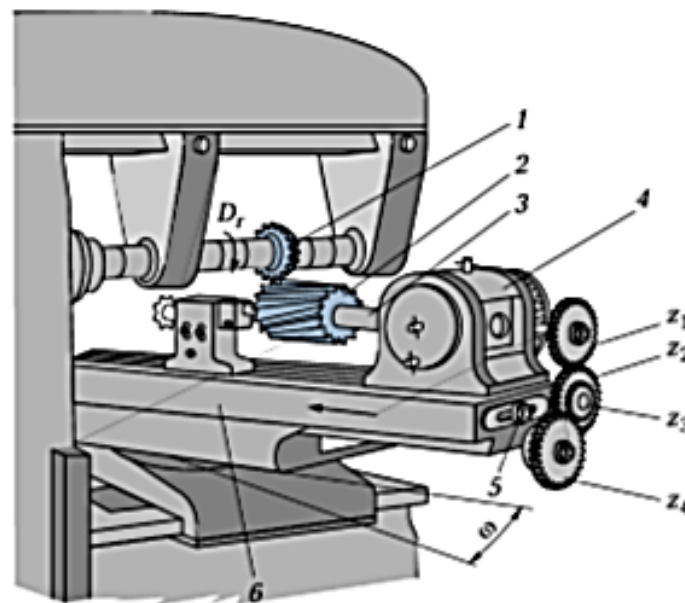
Фрезерование винтовых канавок дисковой фрезой: 1 — фреза; 2 — заготовка; 3 — оправка; 4 — делительная головка; 5 — гитара сменных зубчатых колес; 6 — стол фрезерного станка; z_1 – z_4 — число зубьев сменных зубчатых колес; D_r — направление главного вращательного движения; ω — угол поворота стола станка
